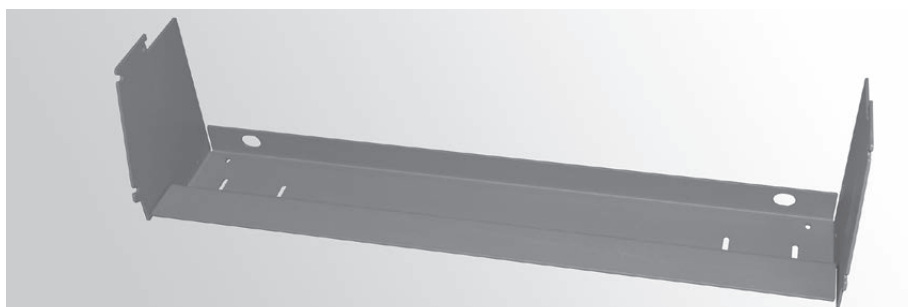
Elemento di collegamento superiore (illustrazione PuroWIN PWPE 60)
